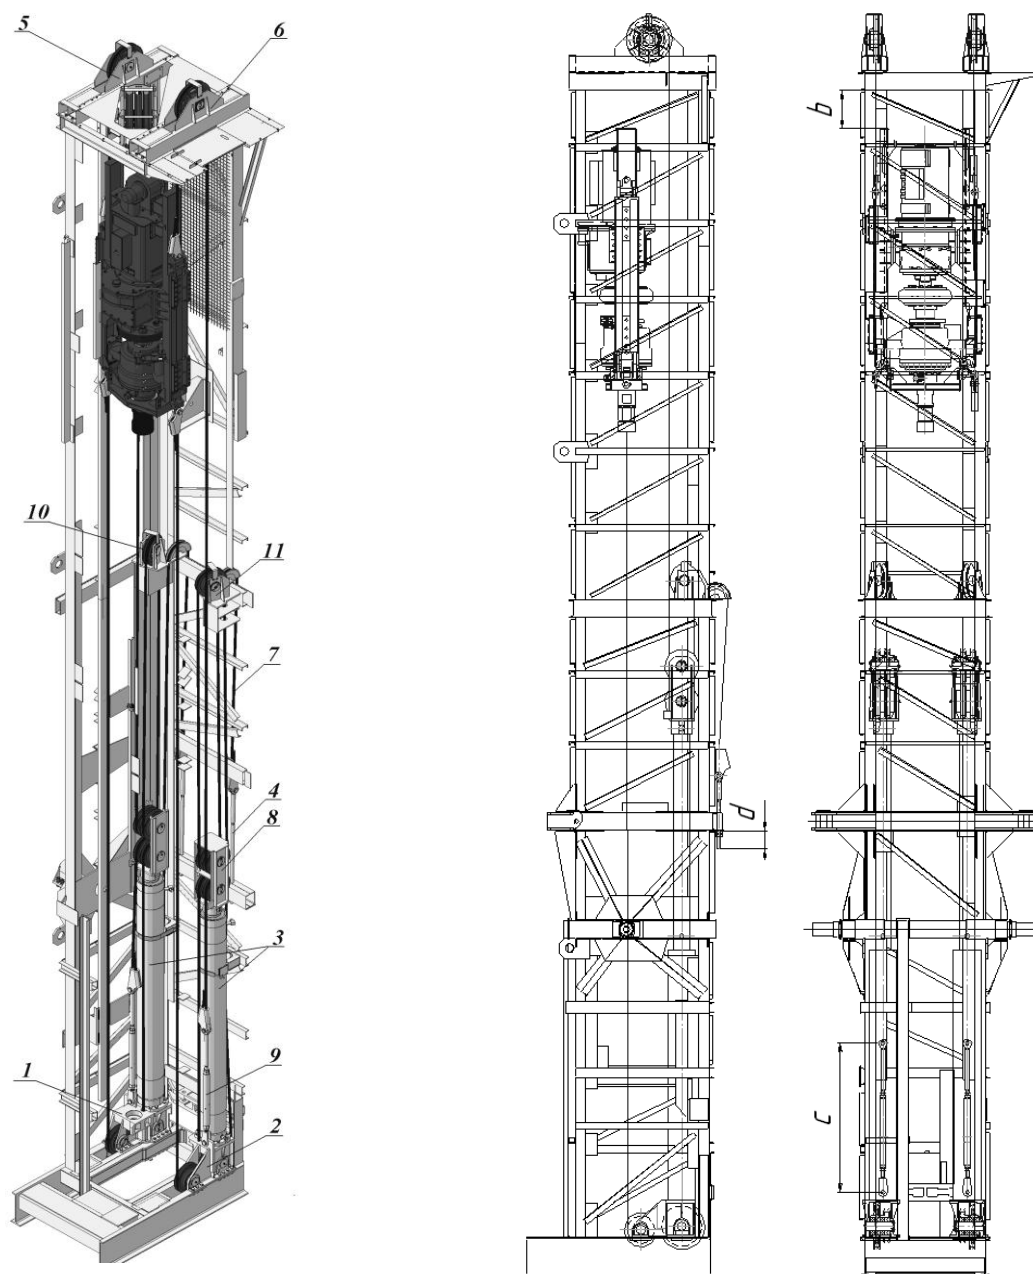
Вращательно-подающий механизм станка СБШ-270/311 КП: 1 – блоки нижние правые; 2 – блоки нижние левые; 3 – цилиндр подачи; 4 – винт натяжной; 5 – опора блоков правые;; 6 – опора блоков левая; 7 – канат; 8 – блочная обойма; 9 – муфта стяжная
